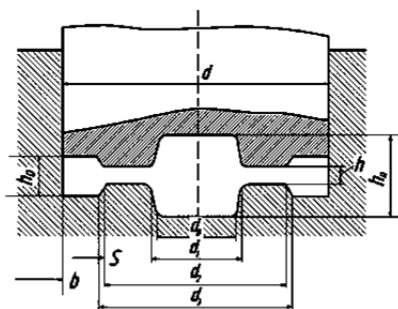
Схема заключительной фазы штамповки детали типа шестерни
